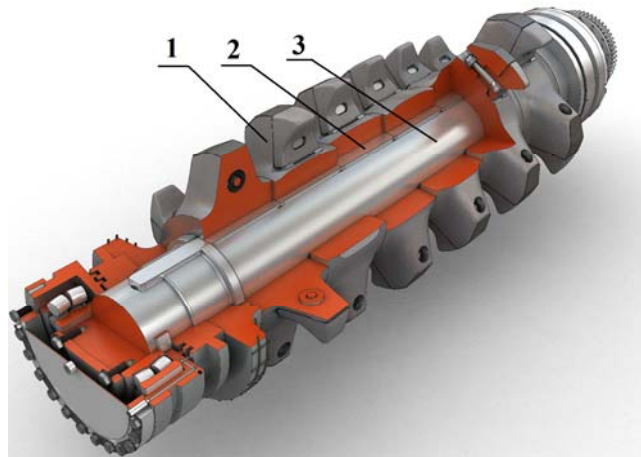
Схема закрепления дисков зубчатых на валу шнека:
